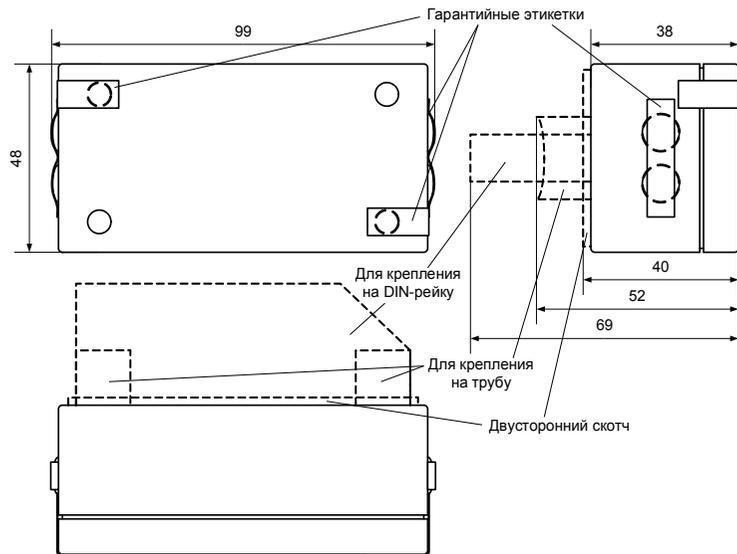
Внешний вид, габаритные и установочные размеры счетчика «Борей 4»
